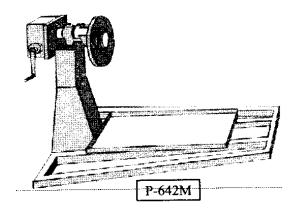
Стенд для сборки и разборки двигателей 3-642М
